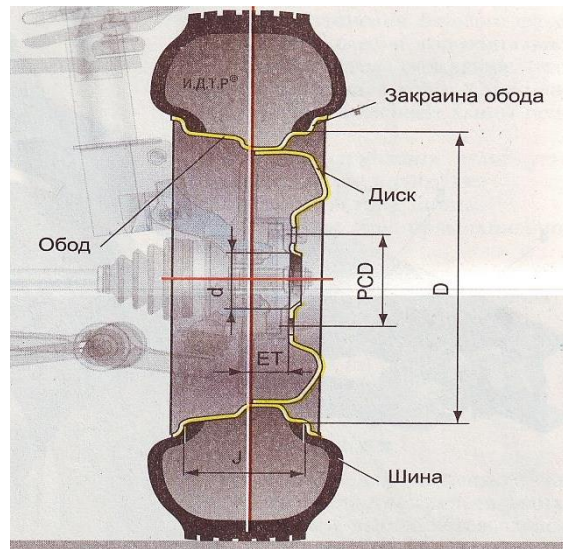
Общее устройство колеса легкового автомобиля:
